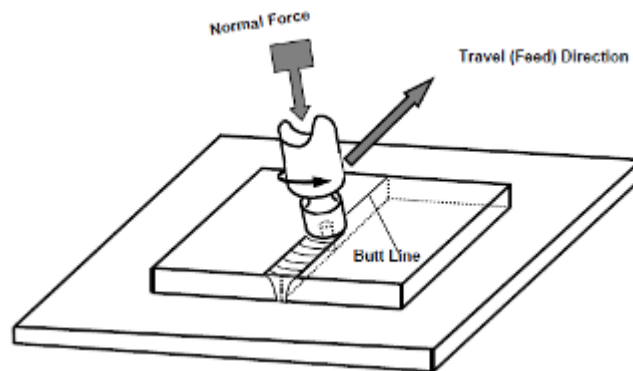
Prinsip Friction Stir Welding (FSW)
